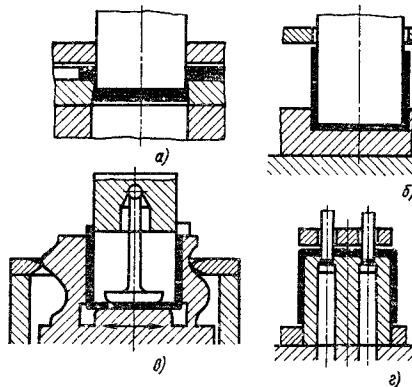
Технологические переходы штамповки коробчатых деталей: а — вырубка заготовки; б — обратное выдавливание; в — обрезка стенок по высоте; г — пробивка отверстий в дне
